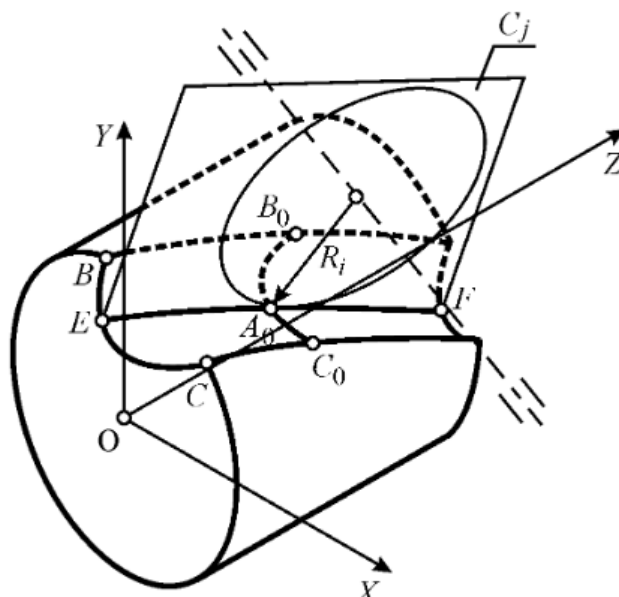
Схема касания ПП инструмента с ВП детали
